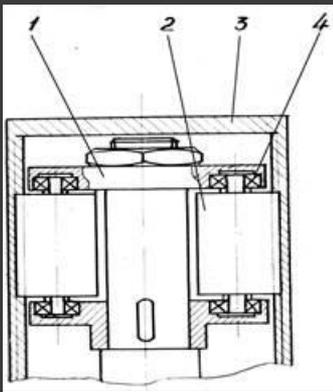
Передача винт-водило с резьбовыми роликами – гайка-шток: 1 – водило; 2 – резьбовые ролики; 3 – гайка-шток; 4 – подшипники
